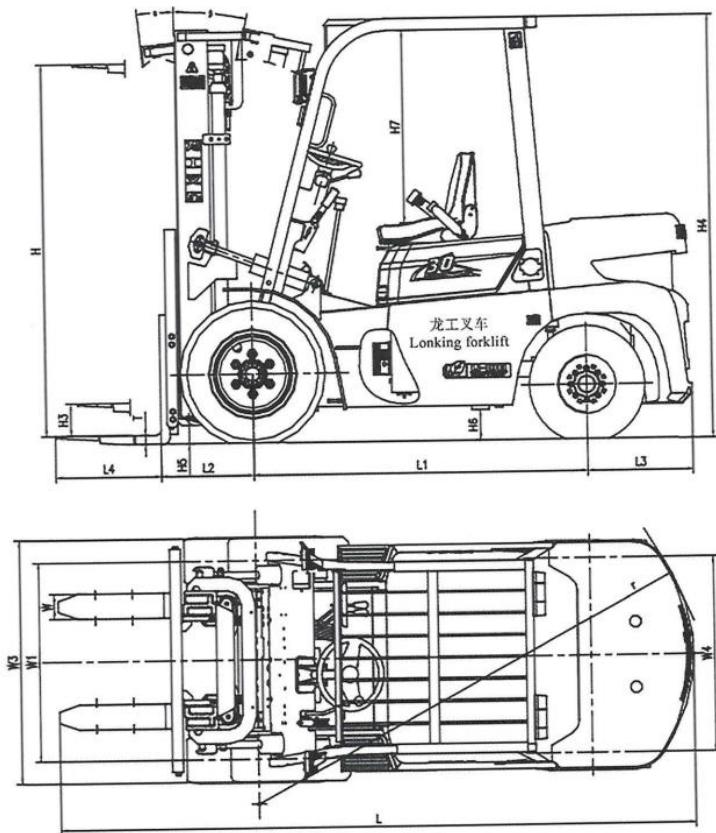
Чертеж общего вида вилочного погрузчика.
